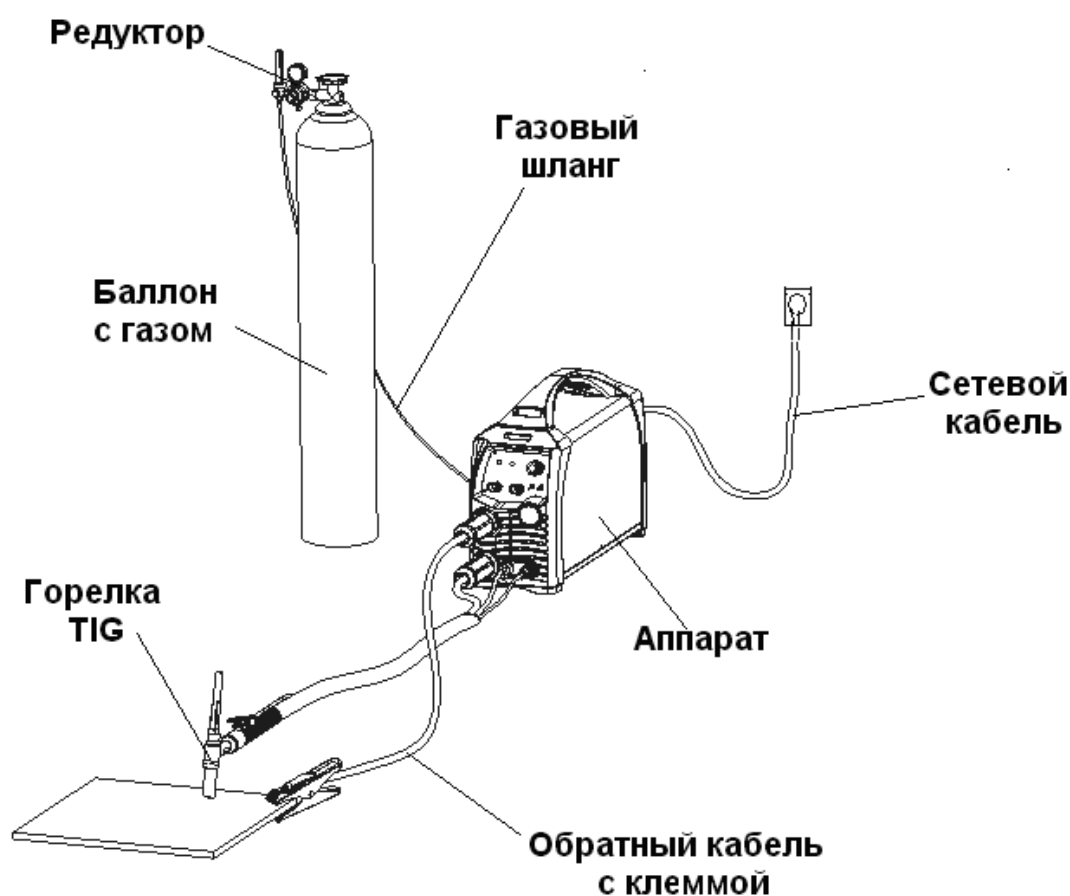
Схема подключения оборудования для TIG сварки
